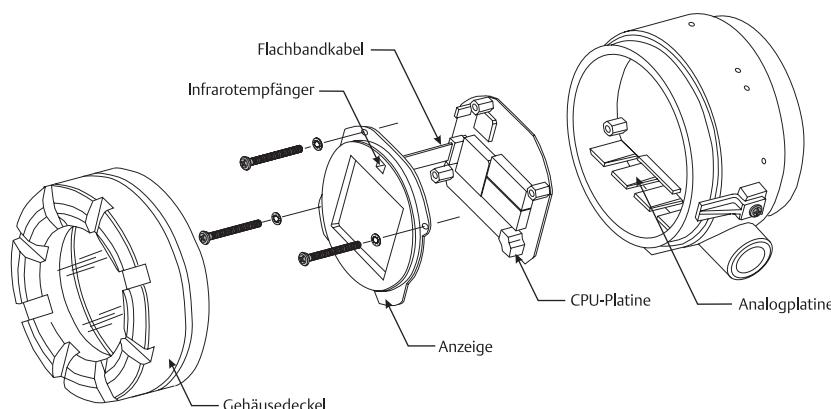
Explosionszeichnung Zweileiter-Messumformer 5081-P-HT
